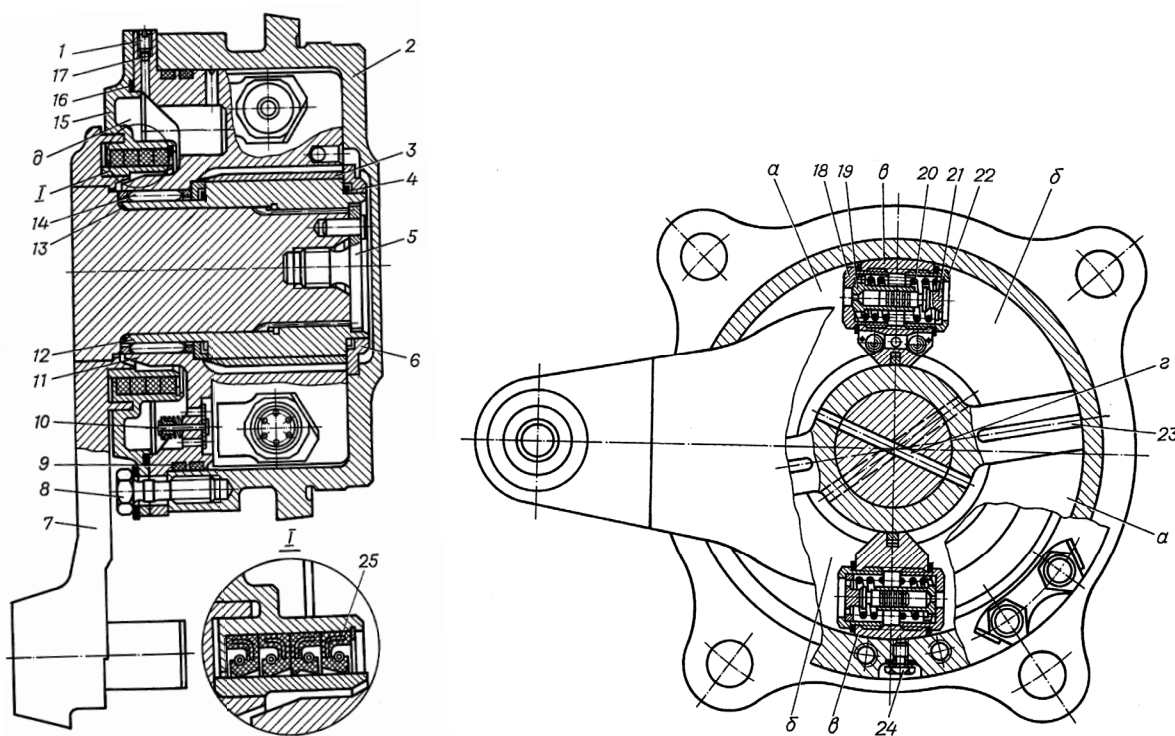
Устройство гидроамортизатора: 1 – винт; 2 – корпус; 3 – вкладыш; 4 – пружинное кольцо; 5, 24 – пробки; 6 – втулка; 7 – рычаг с осью; 8 – болт; 9, 13, 16 – уплотнительные кольца; 10 – тарельчатый клапан; 11 – перегородка; 12 – лопасть; 14 – игольчатый подшипник; 15 – крышка; 17 – шарик; 18 – стакан клапана; 19 – клапан; 20 – пружина; 21 – плунжер; 22 – стакан; 23 – колодка; 25 – манжета; *a*, *б* – рабочие камеры; *в* – выступ перегородки; *г* – отверстие в лопасти и оси рычага; *д* – компенсационная камера
